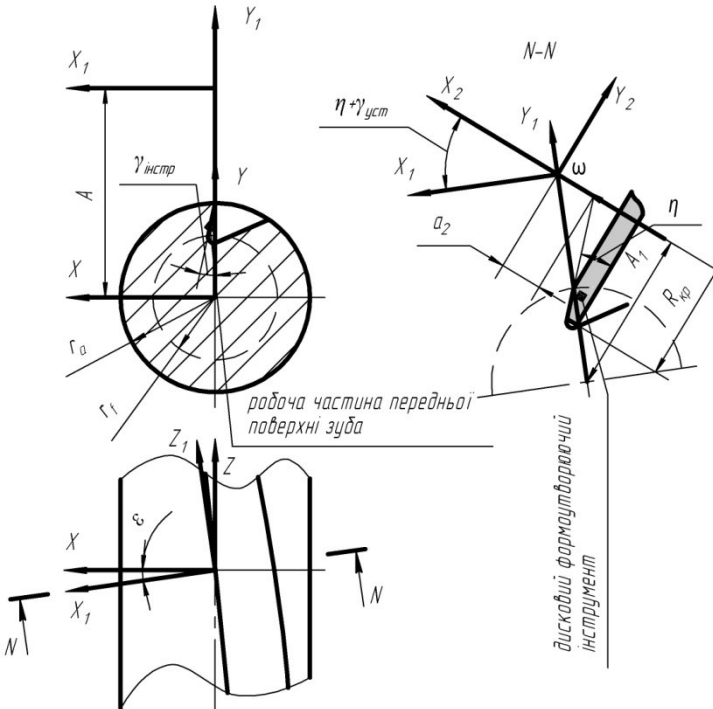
Установка дискового инструмента при утворенні передньої поверхні зуба фрези
